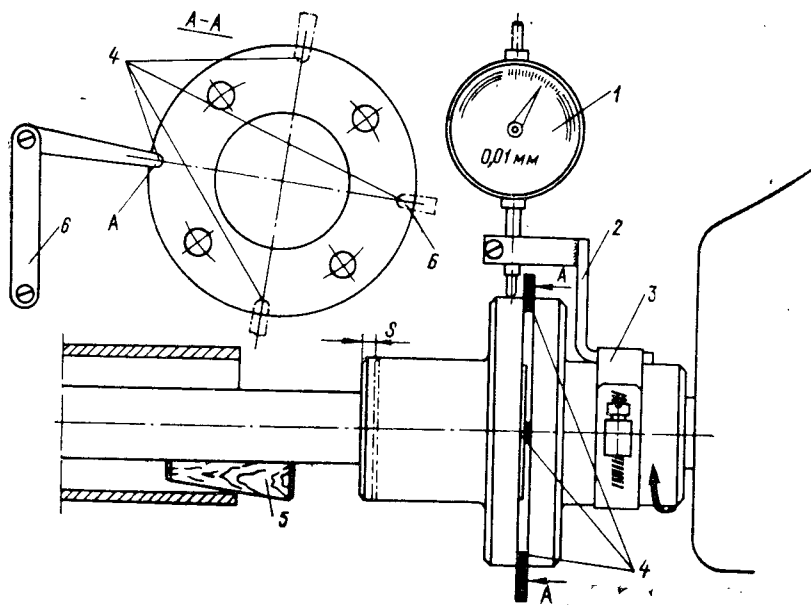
Схема установки индикатора для контроля смещения линии вала и использования щупа для замера излома.
